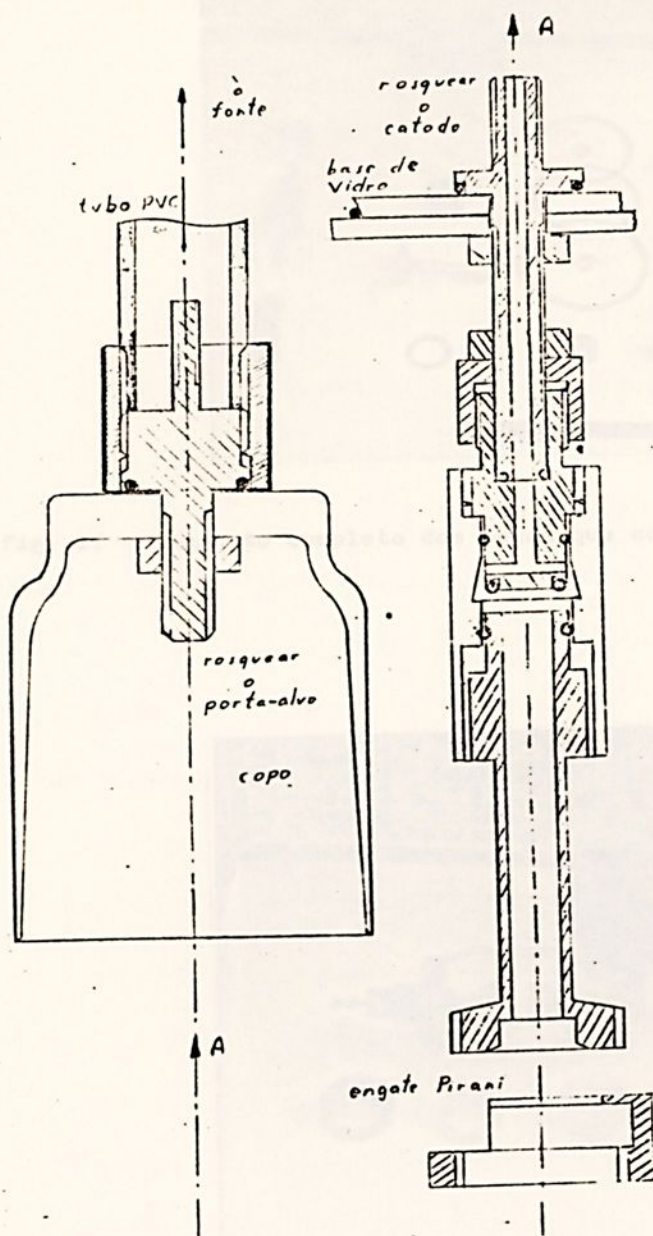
b - Montagem do conjunto envolvendo a ampola, válvula e engate para vácuo.
